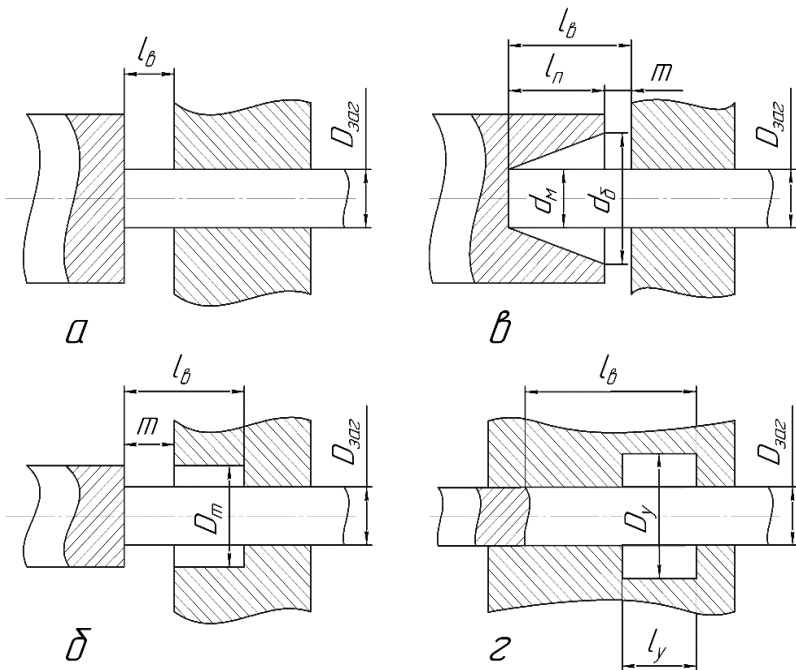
Форма ручьев для набора металла и расположение заготовки в ручье: а – конец заготовки не зажат; б – в цилиндрической матрице; в – в коническом пуансоне; г – конец заготовки не выступает за пределы матрицы
